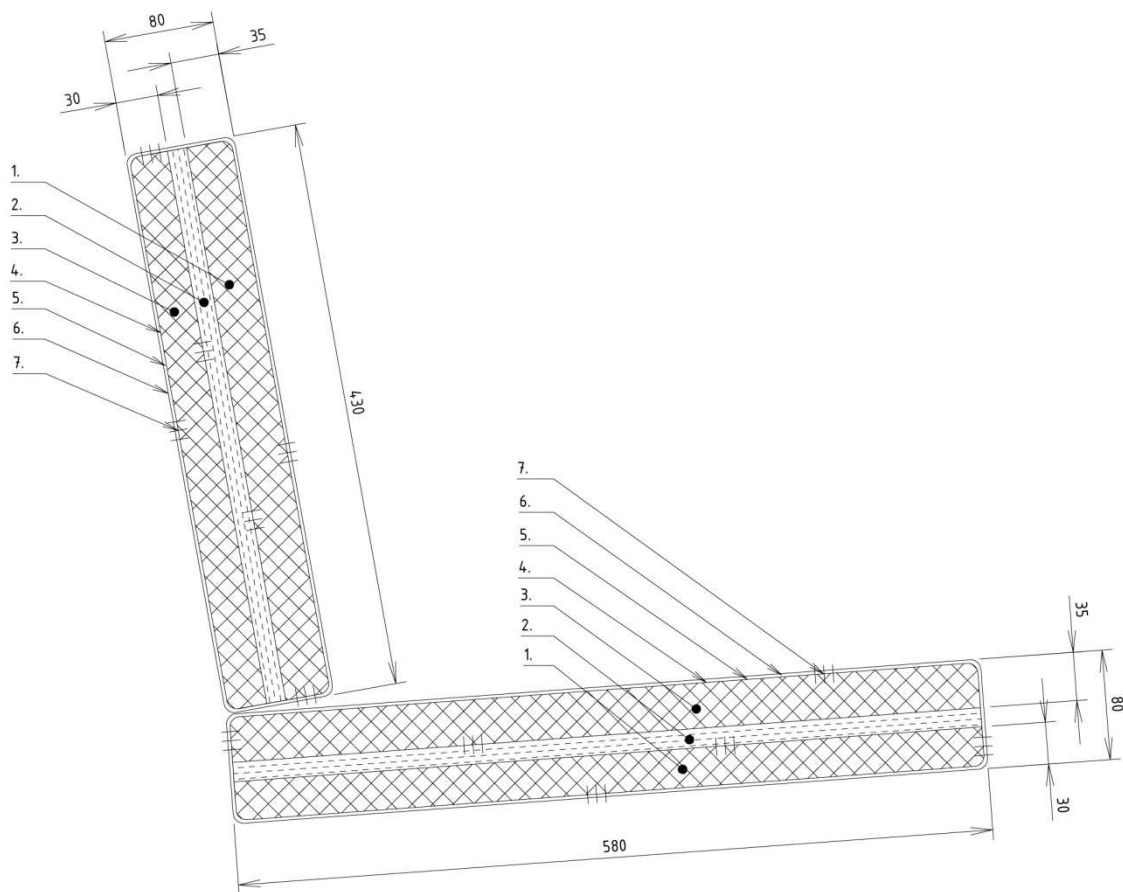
Schematické řezy konstrukcí čalounění – varianta 1
